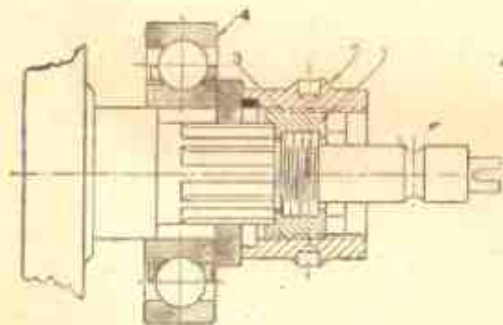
Приспособление для посадки заднего опорного подшипника:
